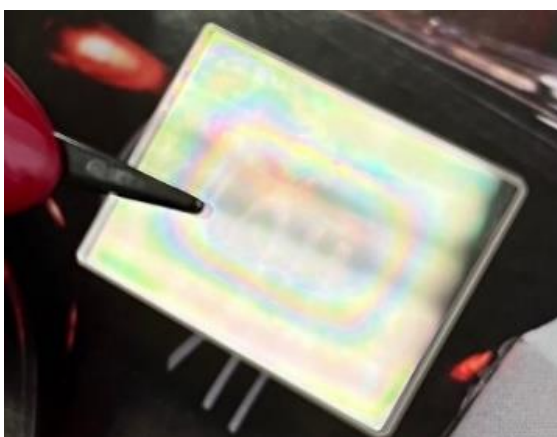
Фото интерференционной картины на тонкой плёнке на поверхности заготовки
